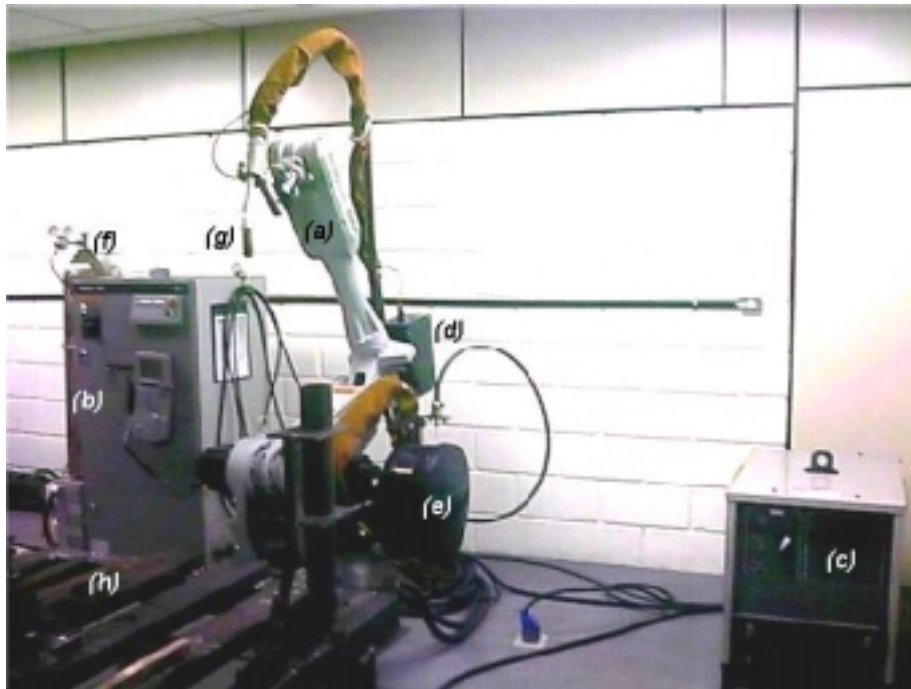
Célula robótica para soldagem – configuração básica. (a) robô; (b) controle; (c) fonte de soldagem; (d) alimentador de arame; (e) rolo de arame; (f) cilindro de gás; (g) tocha de soldagem e (h) mesa de soldagem
